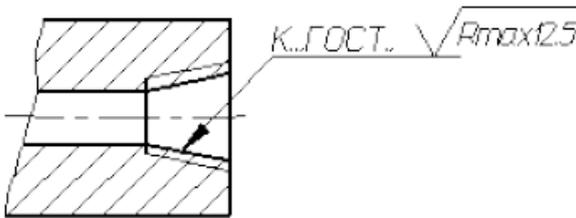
Пример обозначения шероховатости внутренней конической резьбы
